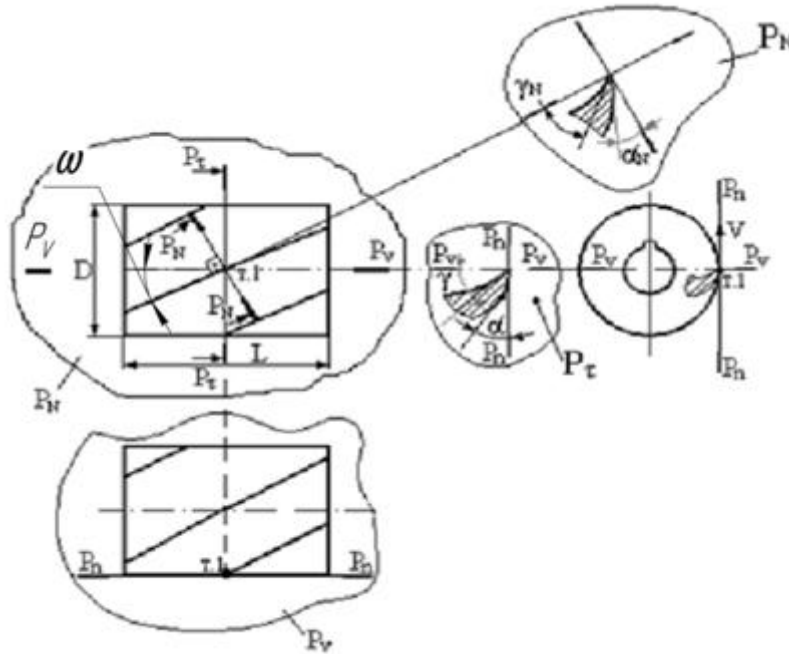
Конструкция и геометрические параметры цилиндрической фрезы
